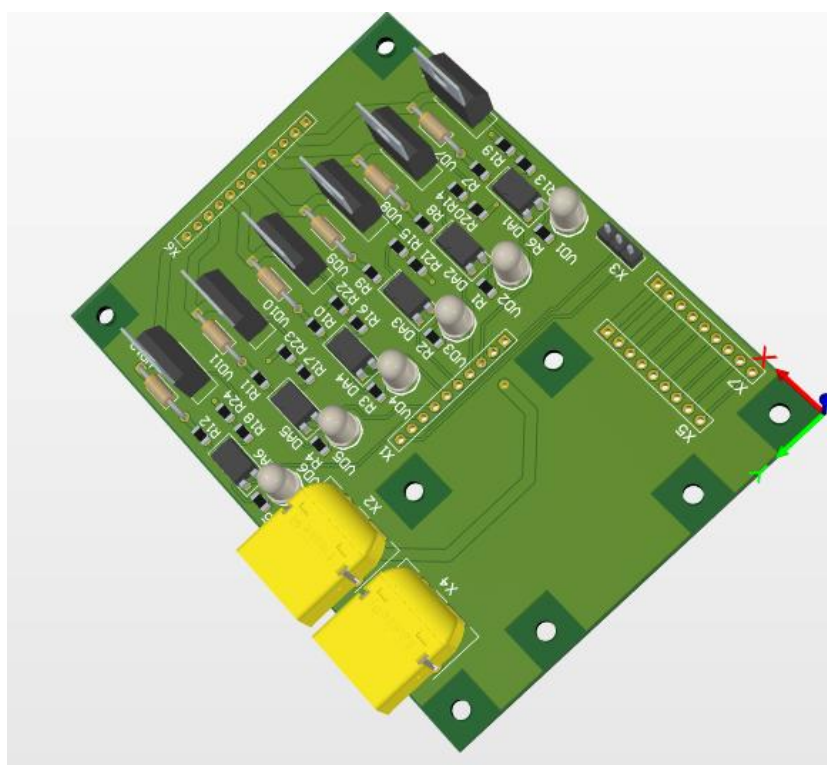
Об'ємний вигляд ДП (верхній шар)
